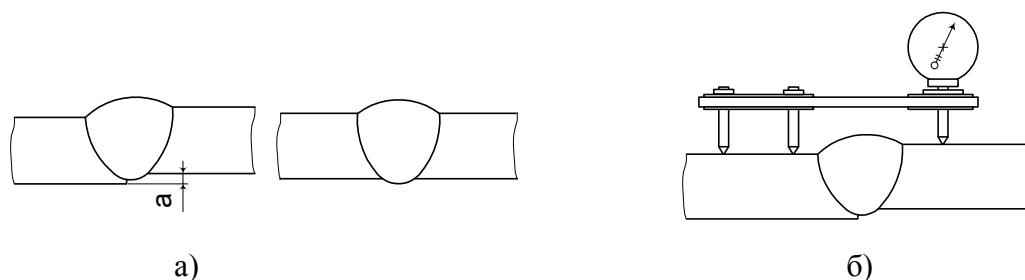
Вид сварного соединения (а) и экспериментальная измерительная установка (б)
